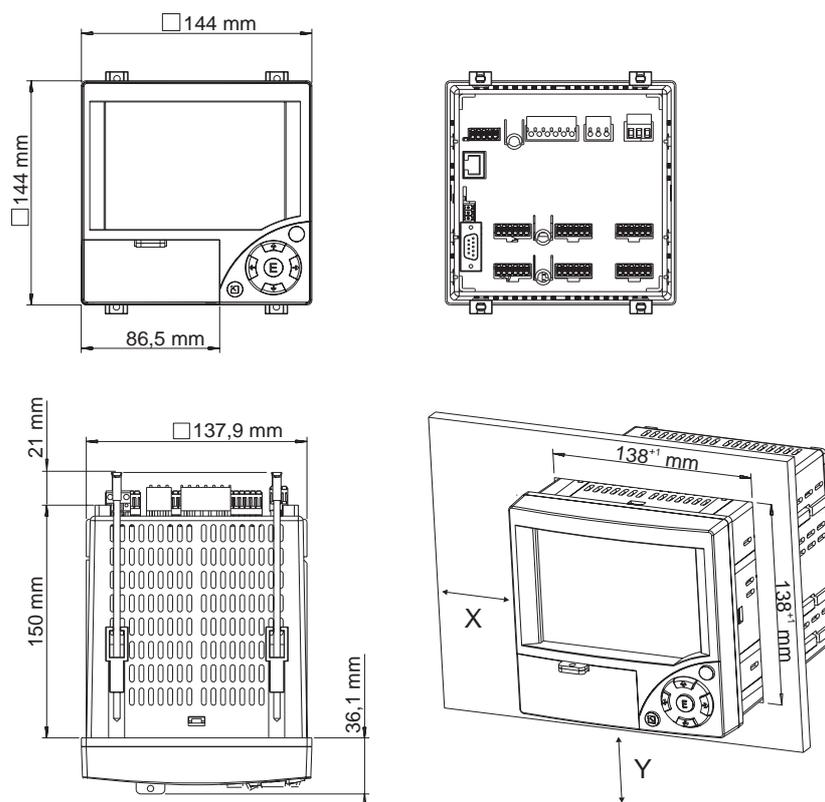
Installazione a fronte quadro e dimensioni di montaggio
